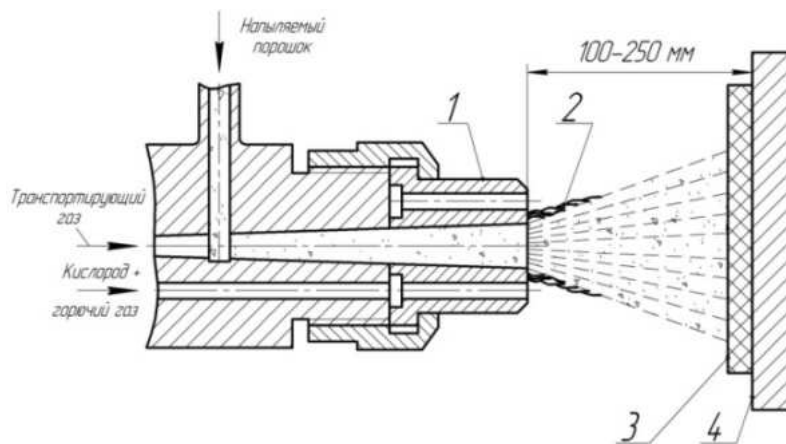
Газопламенное напыление порошкового материала: 1 – сопло; 2 – факел; 3 – покрытие; 4 – подложка
